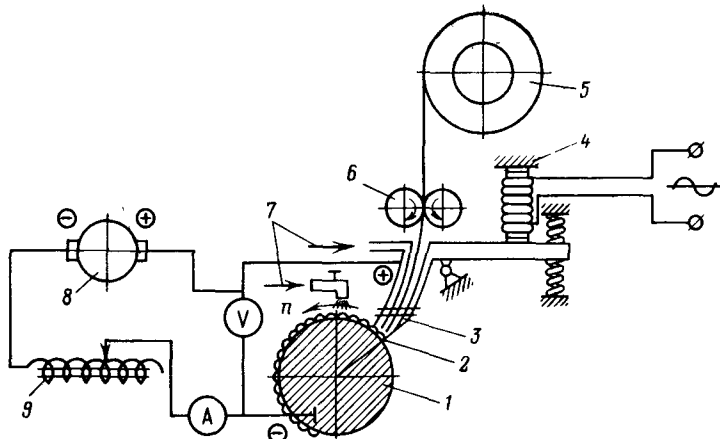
Схема установки вибродуговой наплавки в струе жидкости:
